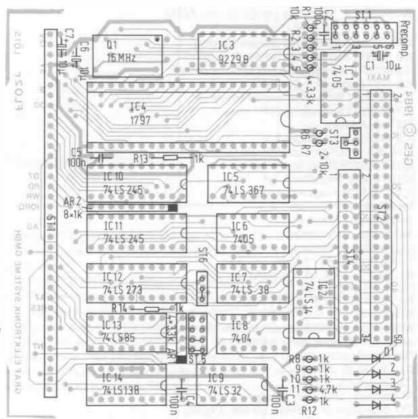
Bestückungsplan der Baugruppe FLO2
